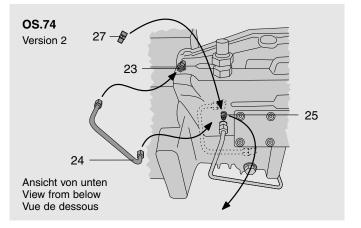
Ansichten OS.74 und Wellenabdichtung (frühere Ausführung)
